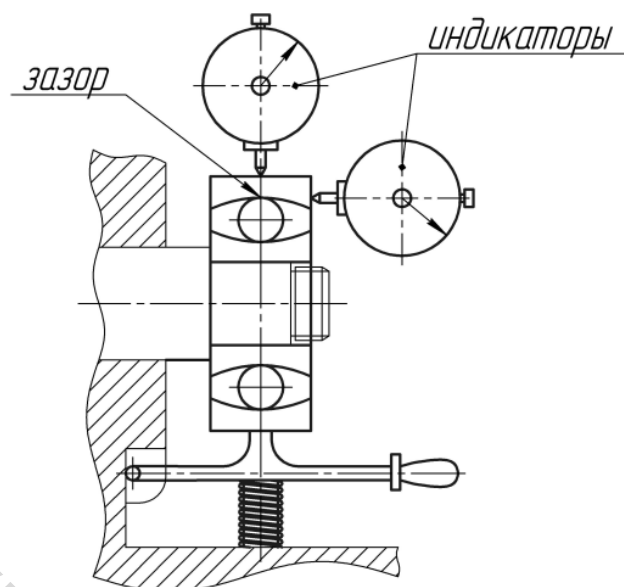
Схема проверки зазоров в подшипнике после его напрессовки на вал
